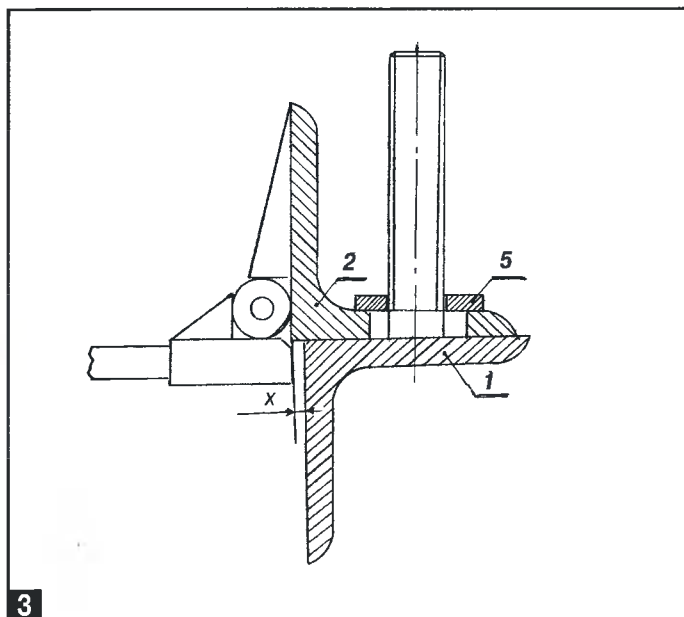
Поперечное сечение станка с зажатой заготовкой:
